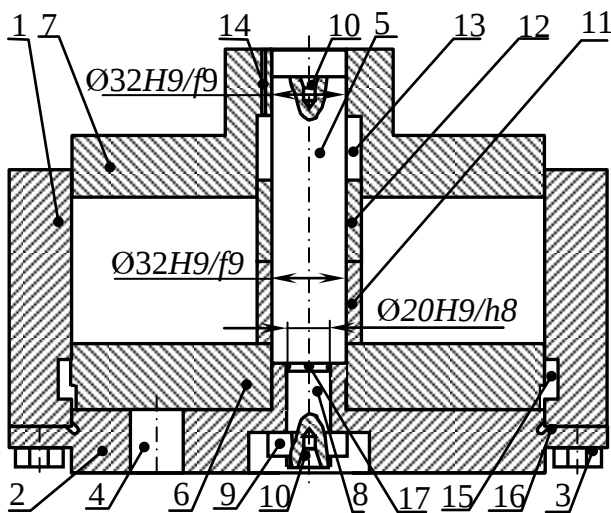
Пресформа для пресування абразивного круга із металевою втулкою
